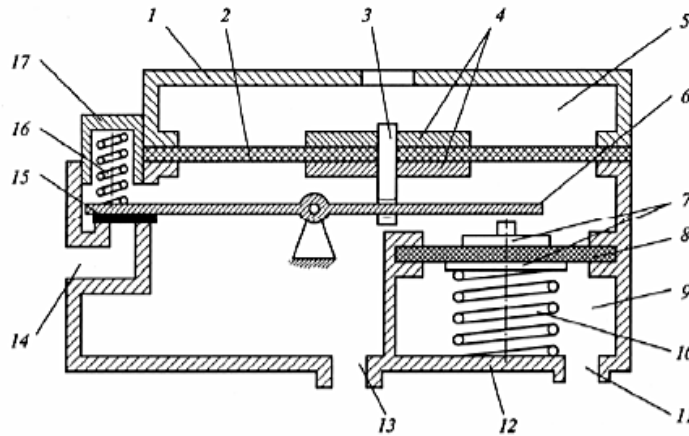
Принципиальная схема 2-й ступени редуктора: 1 - крышка 2-й ступени; 2 - мембрана 2-й ступени; 3 - поводок мембраны 2-й ступени; 4 и 7 - шайбы мембраны; 5 - атмосферная полость; 6 - рычаг клапана 2-й ступени; 8 - мембрана разгрузочного устройства; 9 - полость разгрузочного устройства; 10 и 16 - пружины; 11 - патрубок; 12 - корпус редуктора; 13 - канал выхода газа; 14 - канал входа газа; 15 - клапан; 17 - крышка пружины.
